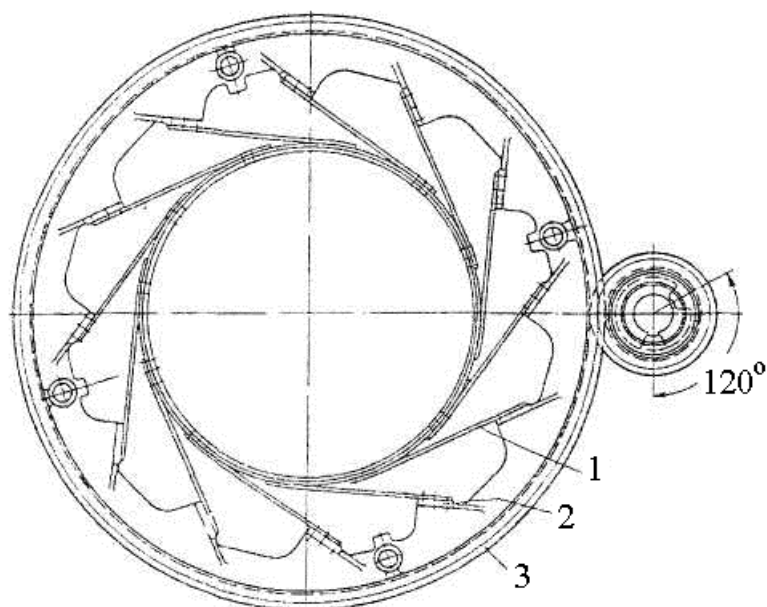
Крепление венцовой шестерни на пластинах:
